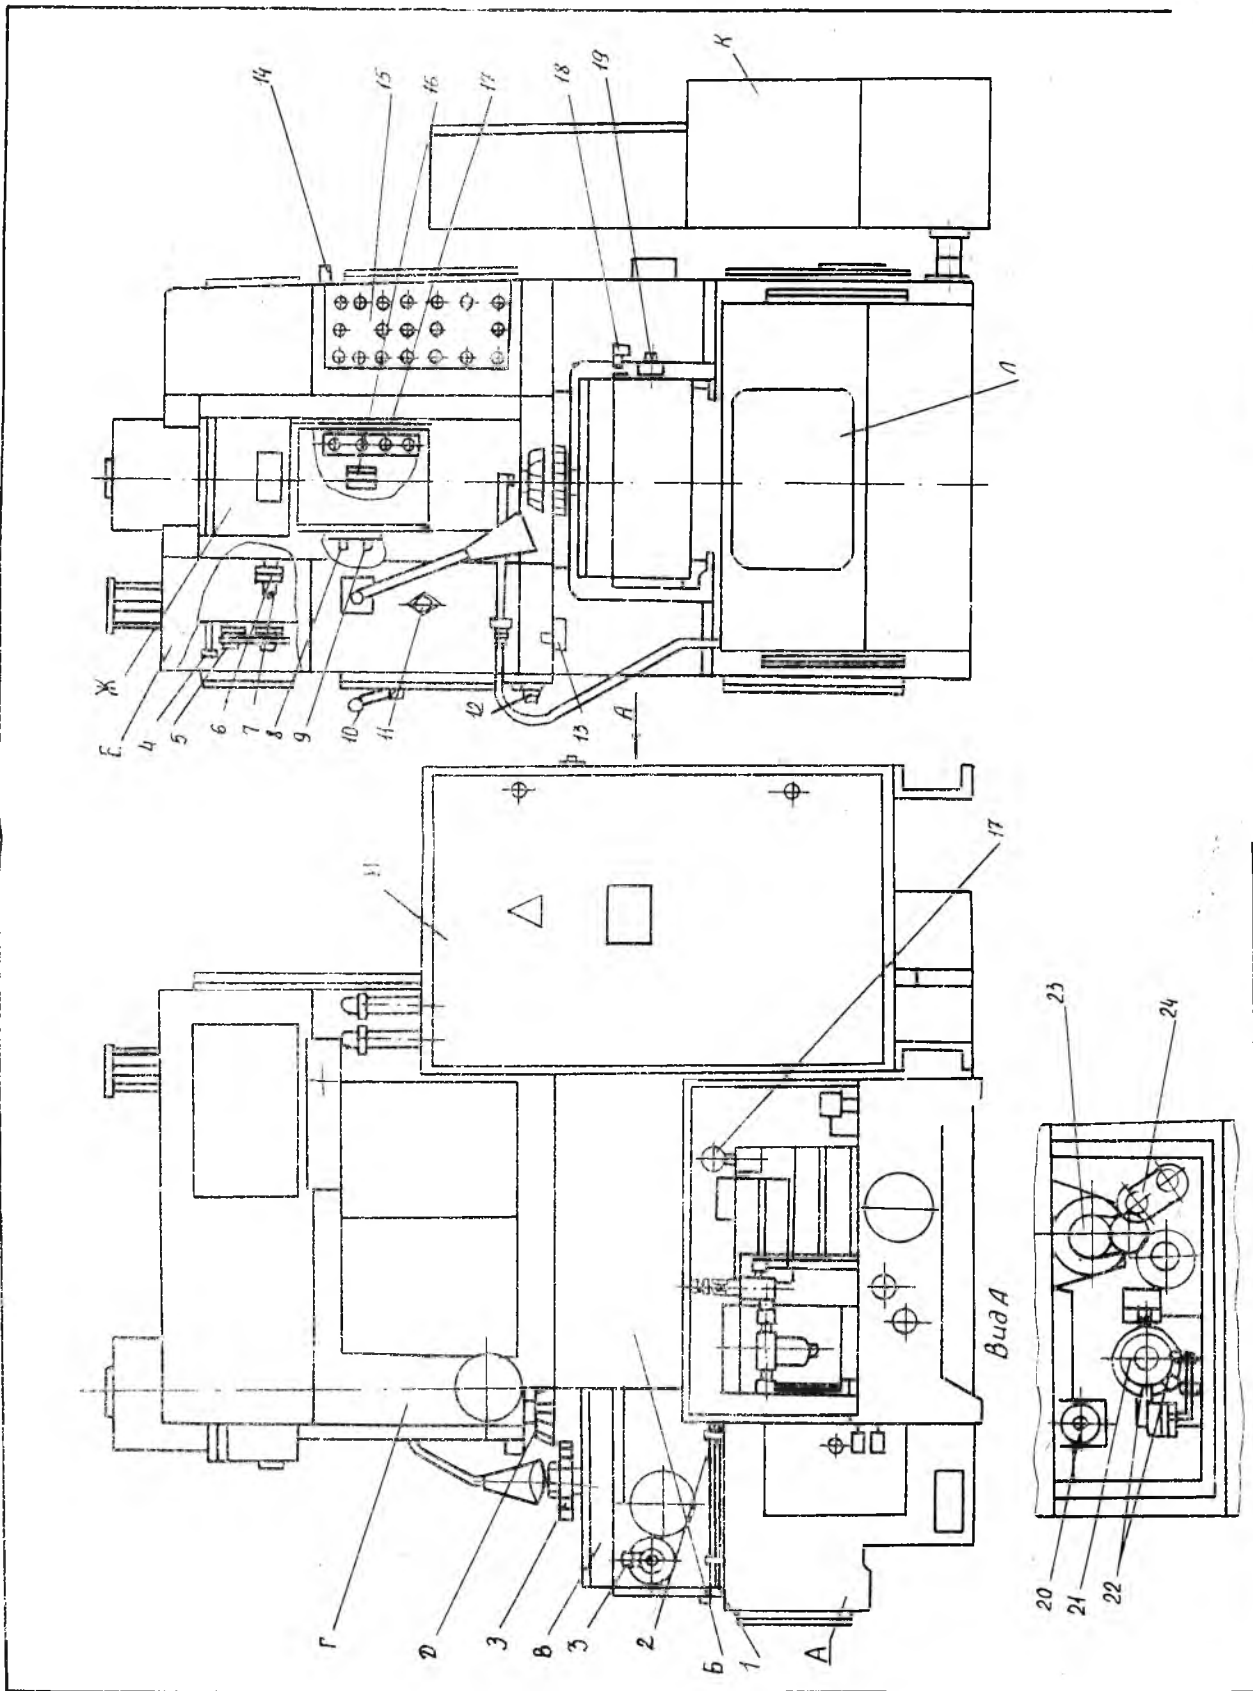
Основные части и органы управления станком: 1, 2 — упоры включения главного привода и выключения привода стола в исходном положении; 3 — лимб настройки межосевого расстояния; 4 — рукоятка реверса цепи деления; 5 — гитара круговых подач; 6 — квадрат поворота шпинделя инструмента; 7 — мелкозубая муфта; 8, 9 — квадраты настройки и фиксации величины хода инструмента; 10, 11 — рукоятка включения и квадрат ручного поворота приводного вала; 12, 13 — квадрат для смещения стойки; 14 — квадрат натяжения ремней главного привода; 15 — пульт управления; 16, 17 — шкала и квадрат для настройки зоны долбления; 18, 19 — шкала и квадрат для настройки межосевого расстояния; 20 — дроссель настройки величины радиальной подачи врезания; 21, 22 — шкала и упоры величины врезания; 23, 24 — гитара деления и приклон для установки паразитного колеса
